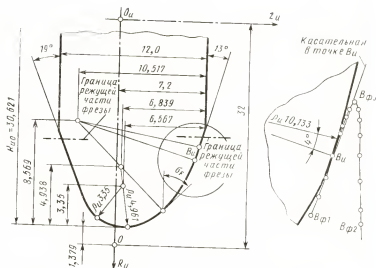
Профиль фрезы для обработки винтовой канавки спирального сверла (параметры сверла в табл. 23)
